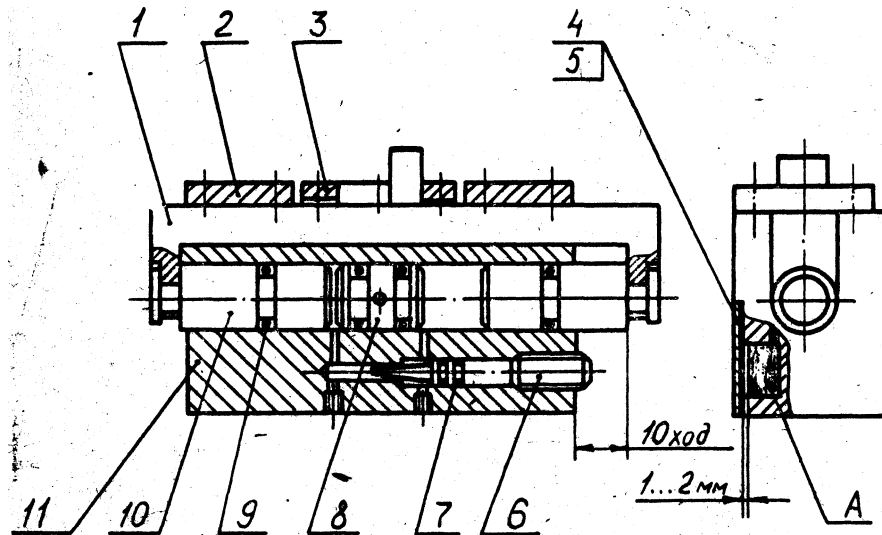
Амортизатор повороту: 1 – скоба; 2 – пластина; 3 – накладка; 4 – кришка; 5 – прокладка; 6 – голка; 7 – кільце гумове; 8 – пробка; 9 – кільце гумове; 10 – шток; 11 – корпус.
